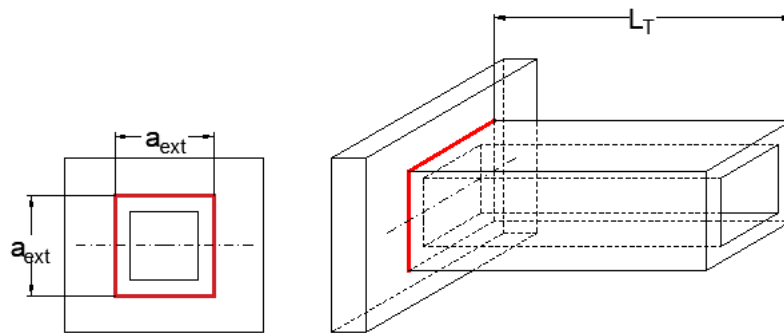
Propiedades flexionantes para soldadura.
